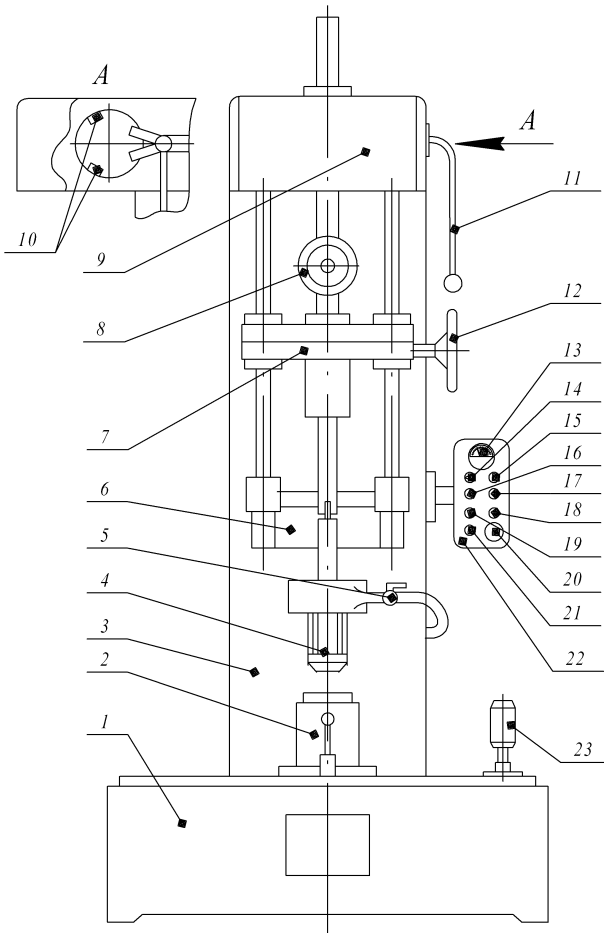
Общий вид вертикально-хонинговального станка 3Г833:
